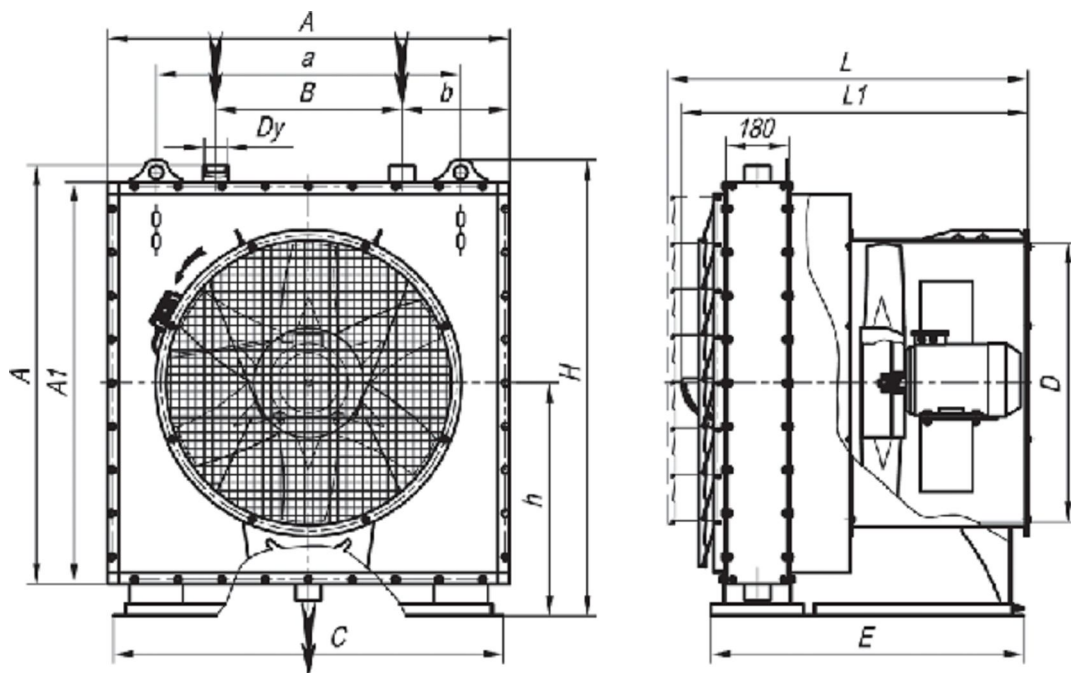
Габаритные и присоединительные размеры агрегатов воздушно-отопительных АО2 №10-25Г на базе воздухонагревателей типа КП.
